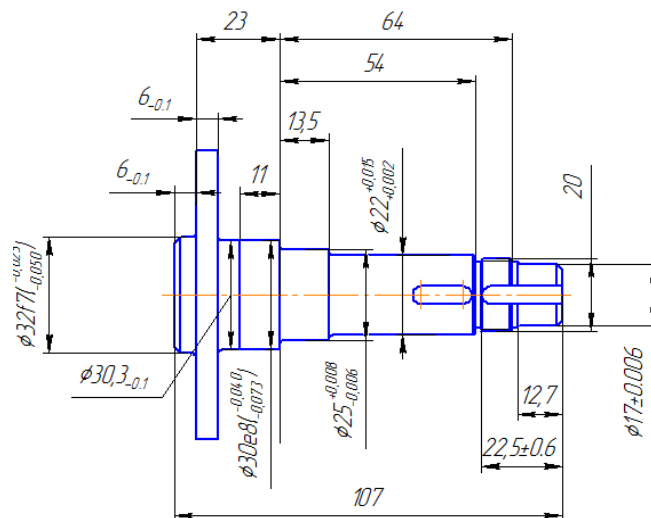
Ескіз деталі з розмірами для проектування заготовки
